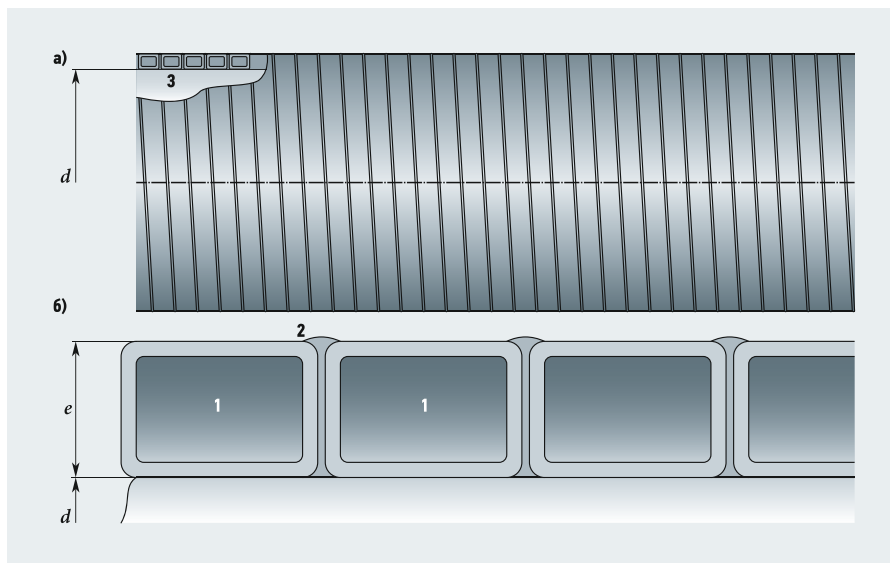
Полиэтиленовая спиральновитая труба «Спиралайн» (а — общий вид трубы, б — продольное сечение А стенки; d и e — внутренний диаметр и толщина стенки; 1 — профиль; 2 — сварной шов; 3 — витки наружной «виртуальной» резьбы)
